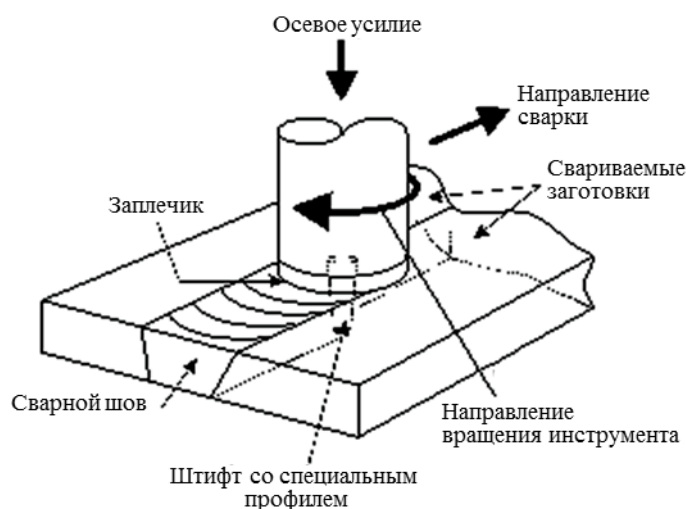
Принцип сварки трением с перемешиванием
